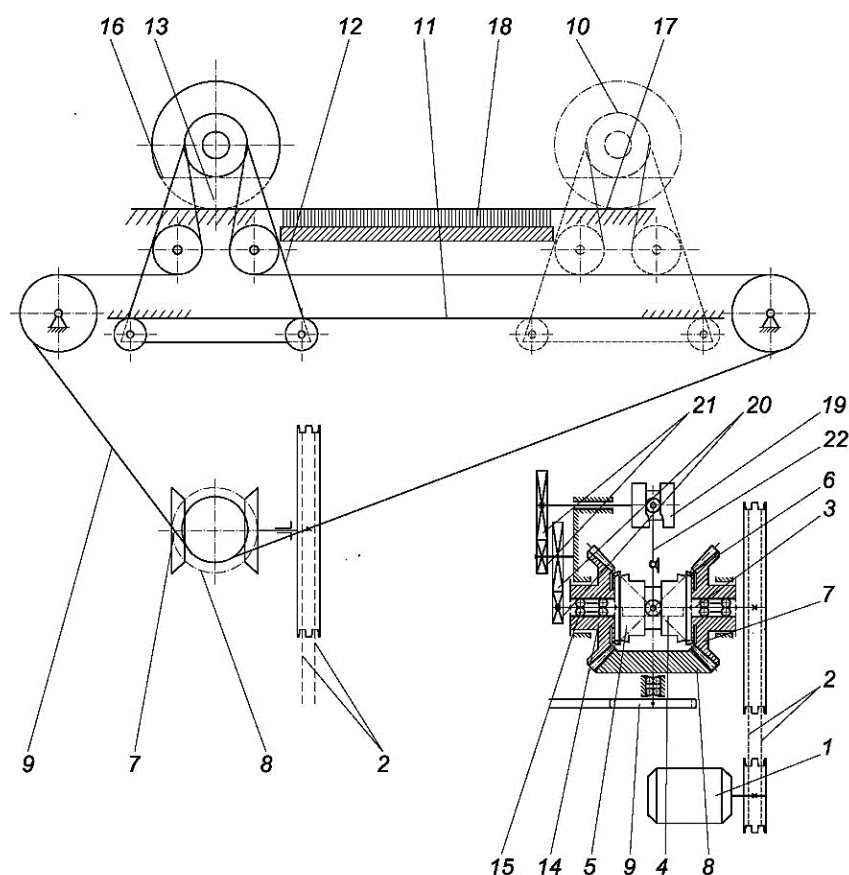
Кінематична схема механізму привода плоскоциліндрового преса:
